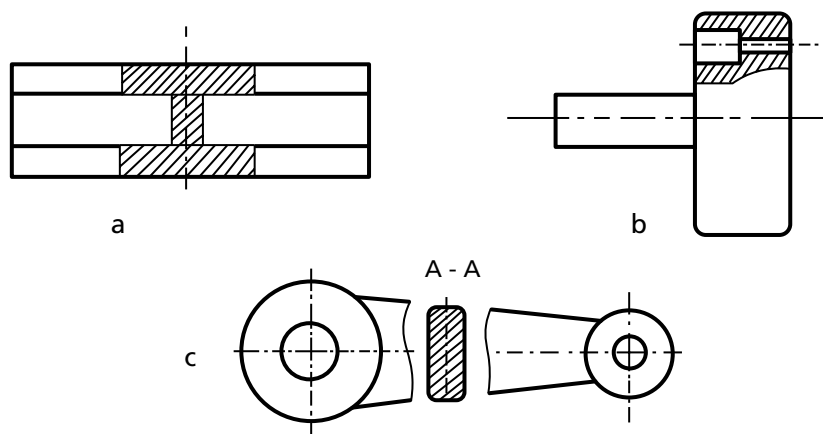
Ejemplo de aplicación de cortes y secciones: a) sección en su sitio; b) corte local; c) sección desplazada
